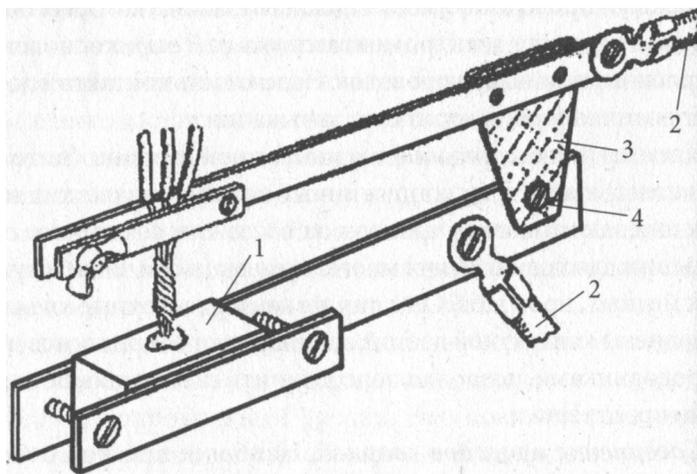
Зажим для сварки жил проводов: 1 — угольный электрод; 2 — шина для подключения к сварочному трансформатору; 3 — изоляционная пластина; 4 — шарнирное соединение
